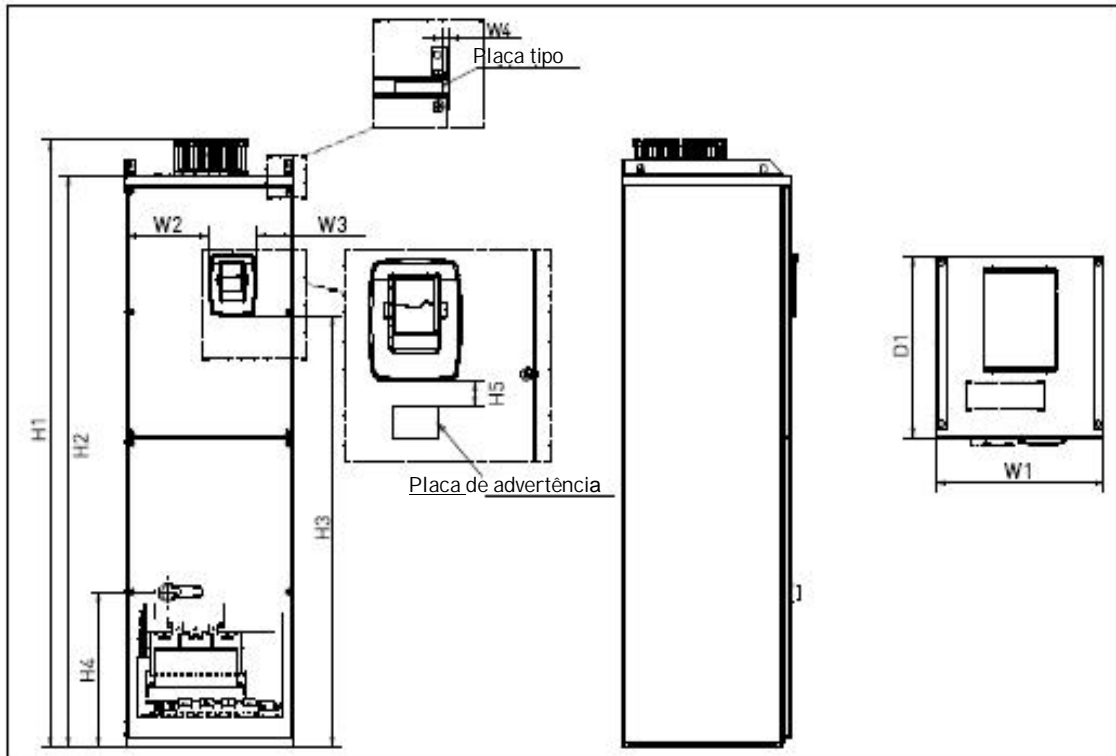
Dimensões do Vacon NX_, FR10 e FR11 (unidades de montagem no piso)
